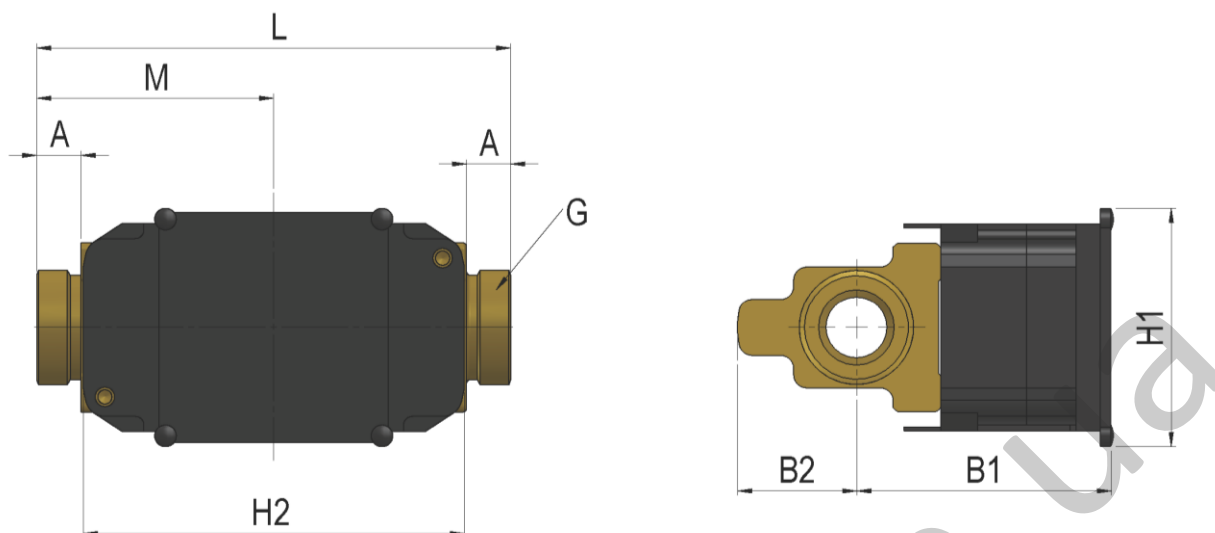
Размерные чертежи ULTRAFLOW® 34 с резьбовым соединением G3/4B и G1B.
